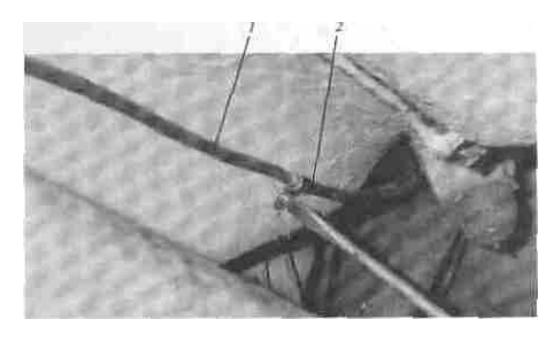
Прокладка трубопровода по днищу кузова: 1- трубопровод; 2- хомут.
